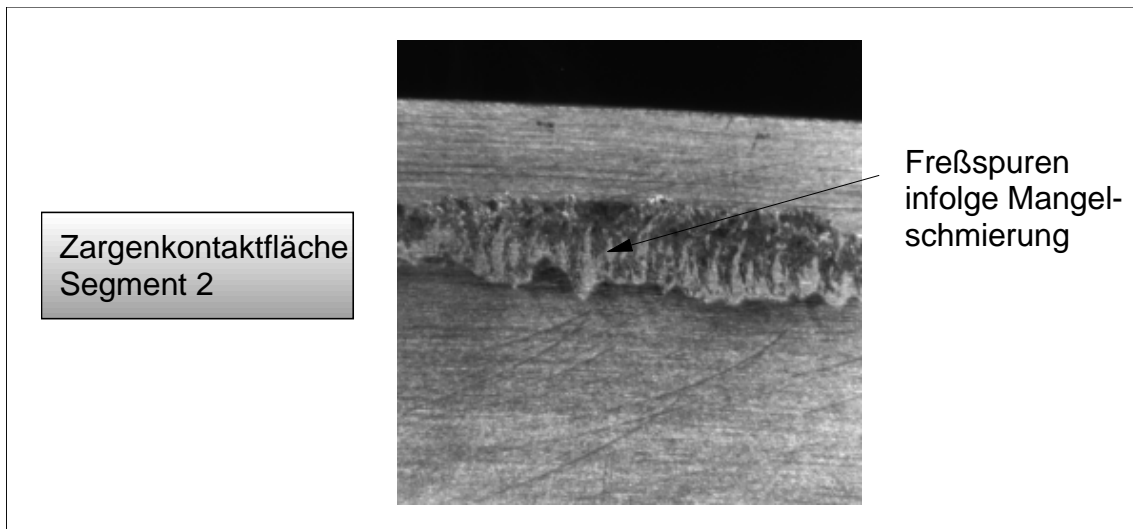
Segmentseitiger Verschleiß der Zargenkontaktfläche
